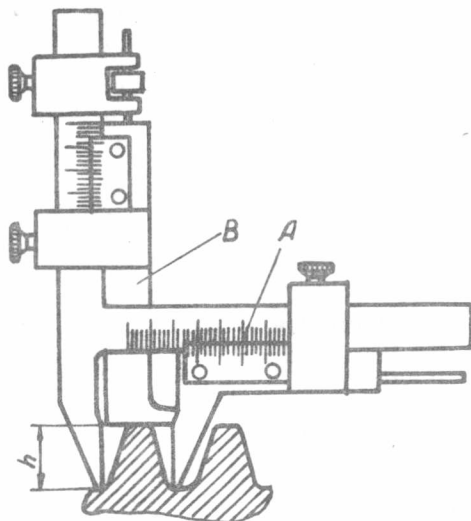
Измерение высоты профиля зуба фрезы зубомером
